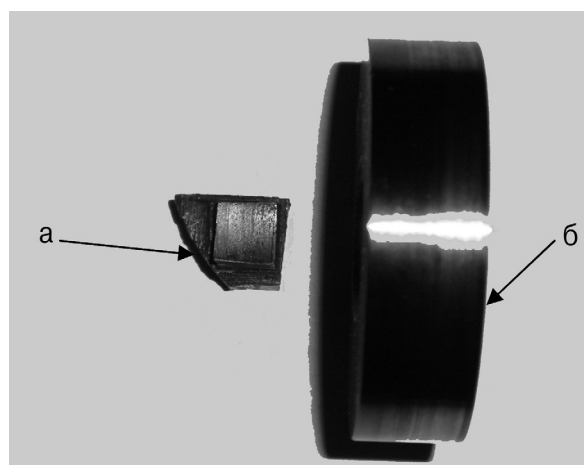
Поверхні тертя після трибовипробувань: а — матеріал композиційного підшипника ДГр10; б — контртіло зі сталі 20Х
